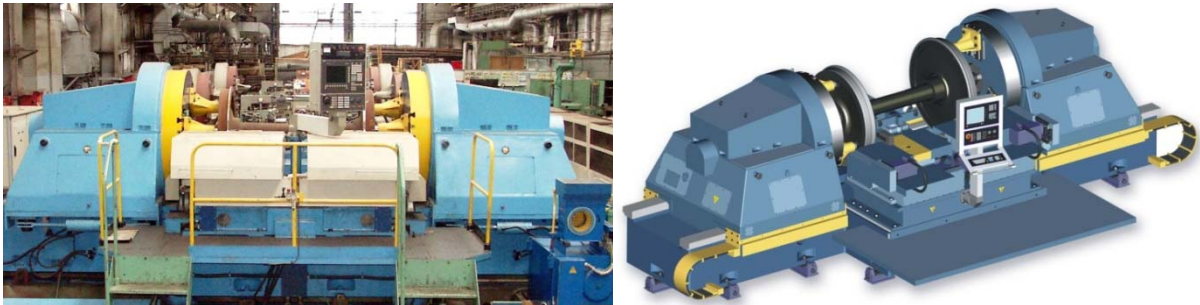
Колесотокарний верстат моделі 1836.10МФ3 з ЧПК
